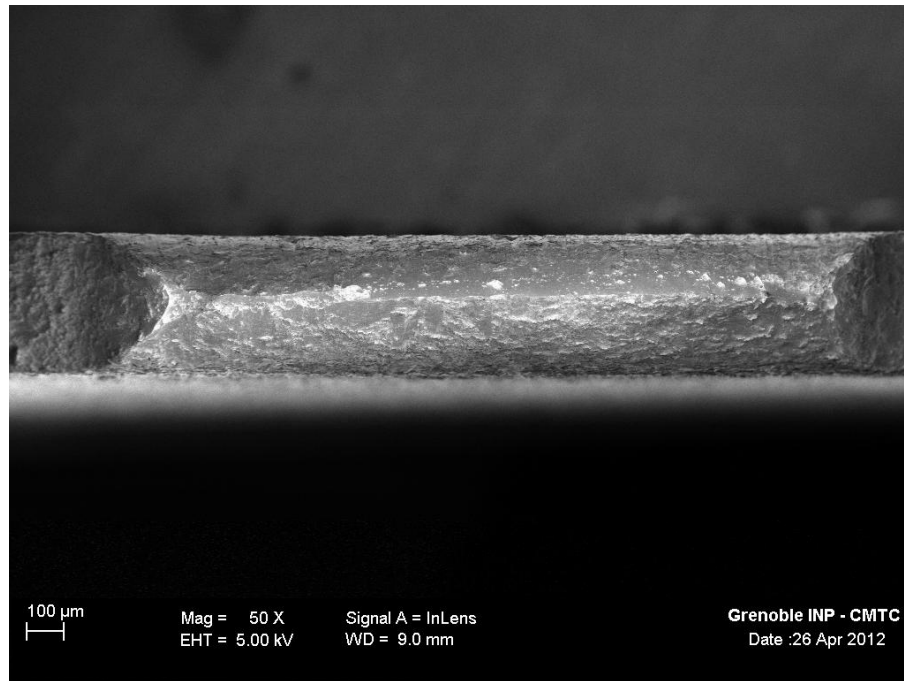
Fractografía de la probeta plana ASTM, con entalle en 60°, de cátodo. Se muestra la zona de fractura que se localiza en el entalle.
